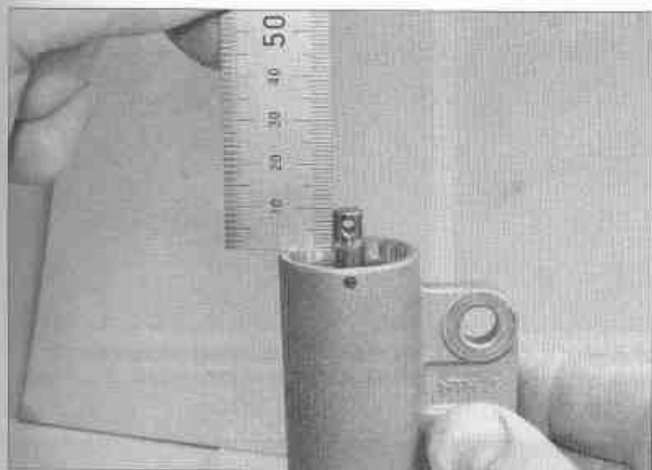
Измерение выступающего штока натяжителя ремня газораспределительного механизма
